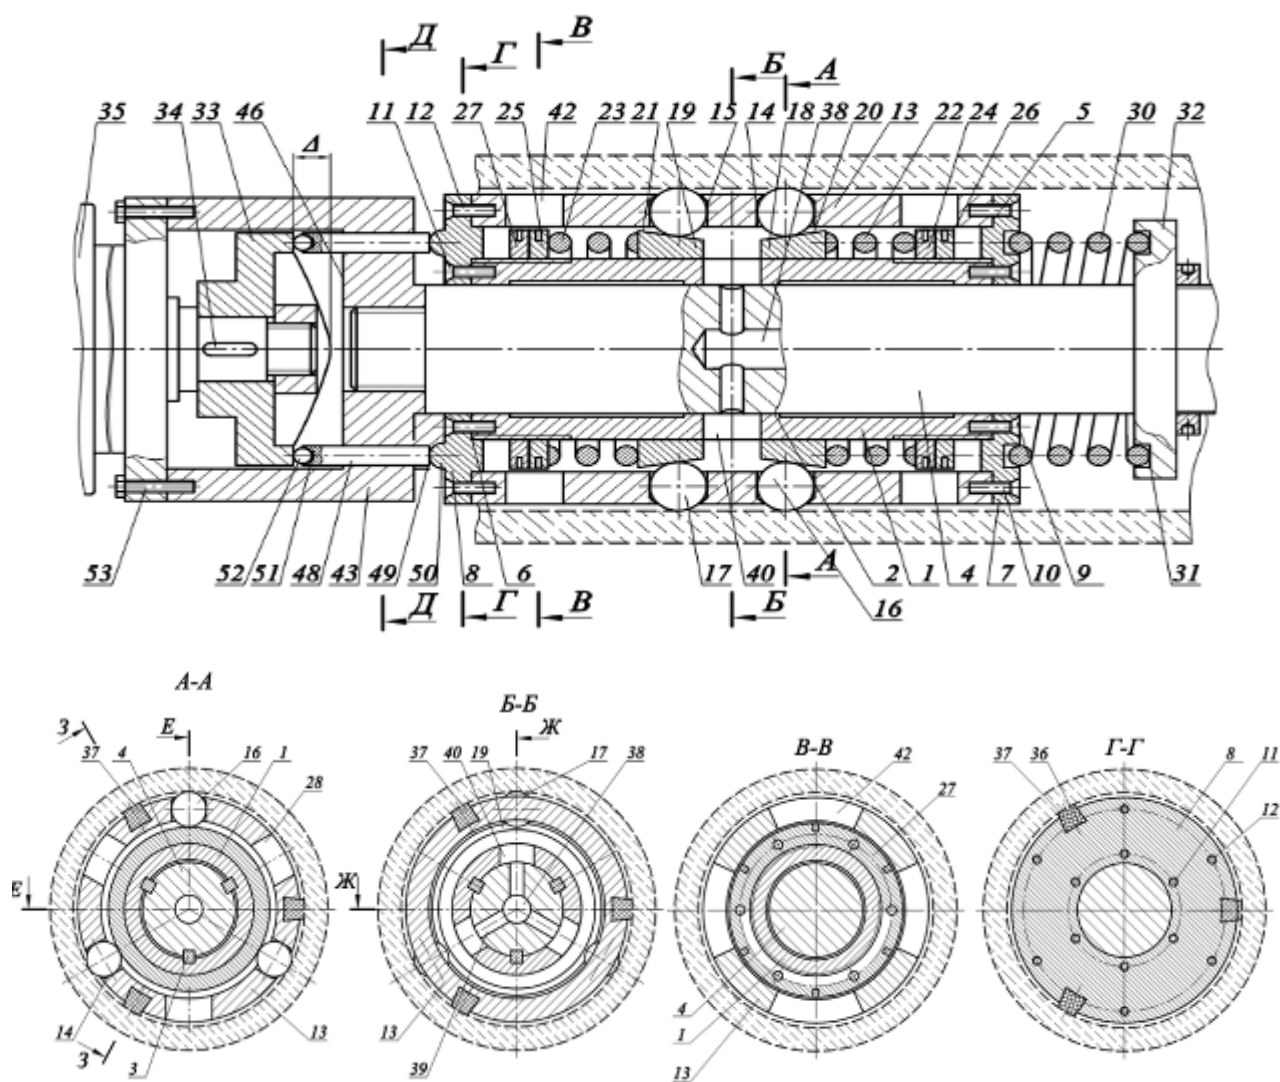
Інструмент для чистового фінішного оброблення внутрішніх циліндричних поверхонь вібраційним обкочуванням [217]
